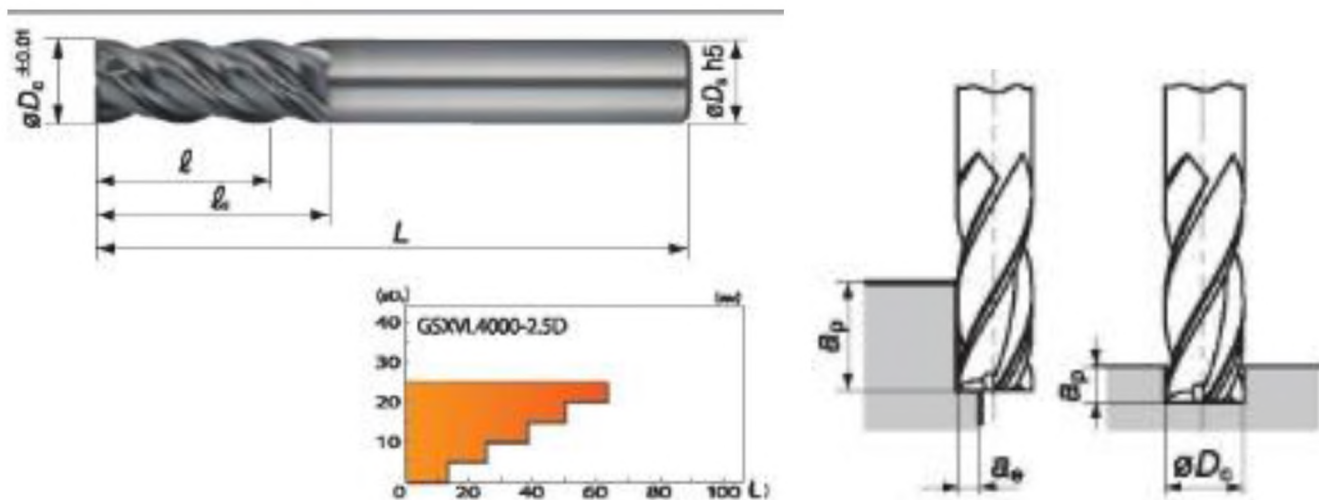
Фреза кінцева GSXVL 4020-2,5D
